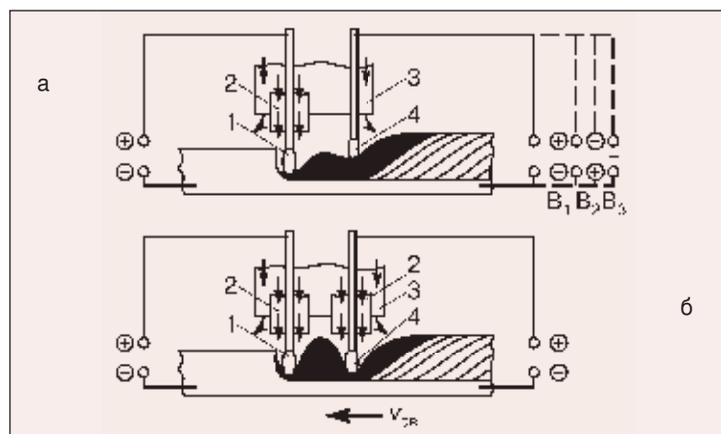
Схема двухдуговой сварки с двухскоростной газовой защитой одной (а) и двух (б) дуг: 1, 4 — соответственно первая и вторая дуга; 2 — сопло для подачи высокоскоростного потока газа; 3 — сопло для подачи защитного газа с обычной скоростью
